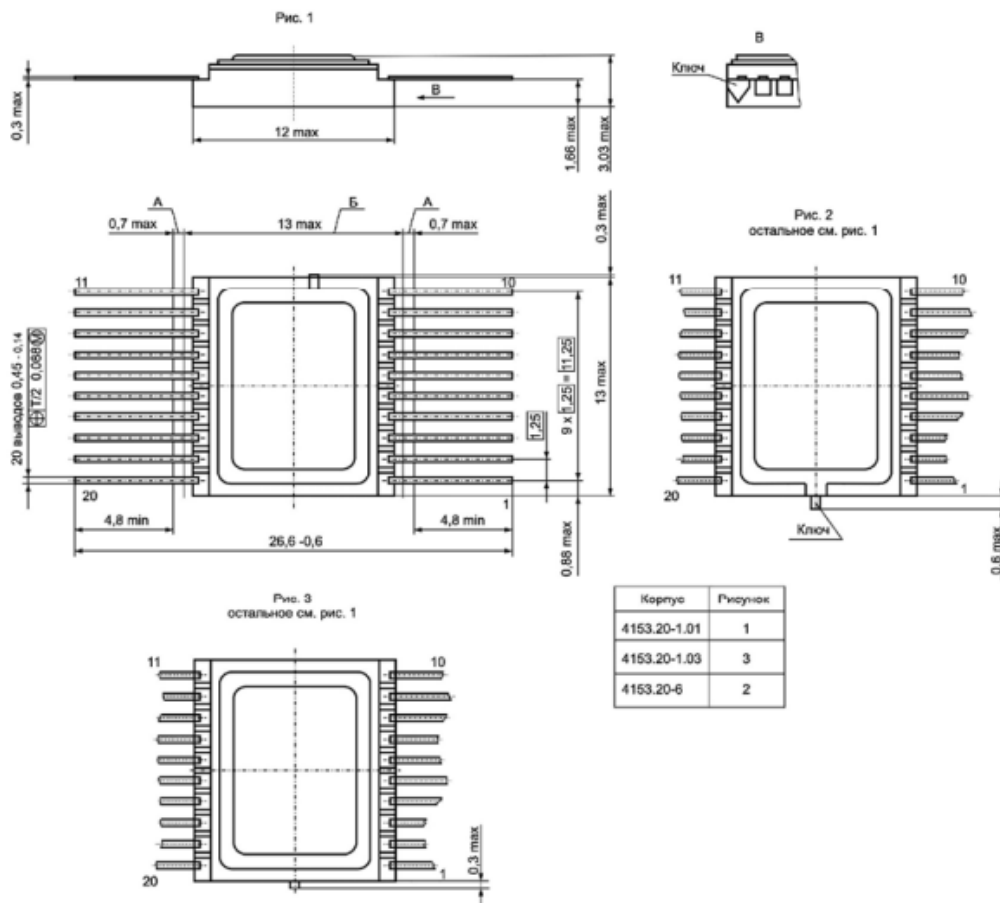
Габаритные размеры корпуса 4153.20-6
